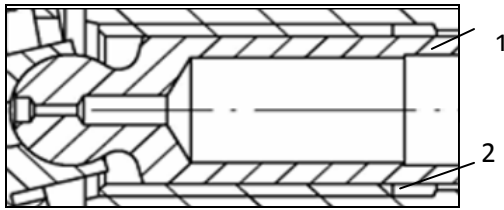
Эскиз типовой пары трения «поршень - стенка цилиндра»
